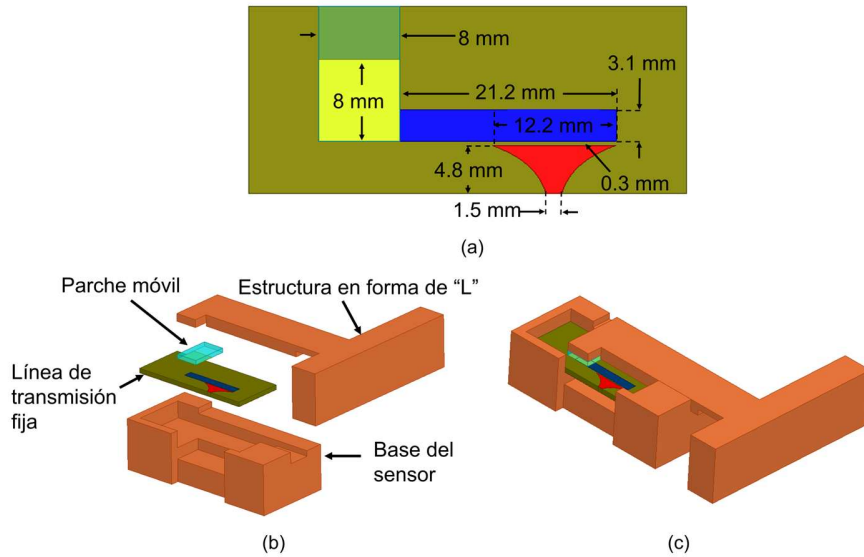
(a) Dimensiones del modelo del sensor propuesto, (b) componentes del sensor y carcasa del sensor, y (c) ensamble del sensor con carcasa creado en HFSS.
